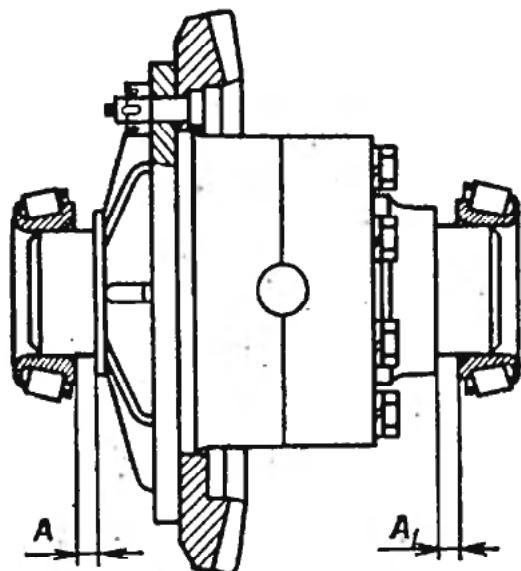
Зазоры A и A_1 между торцами подшипников и коробки сателлитов
